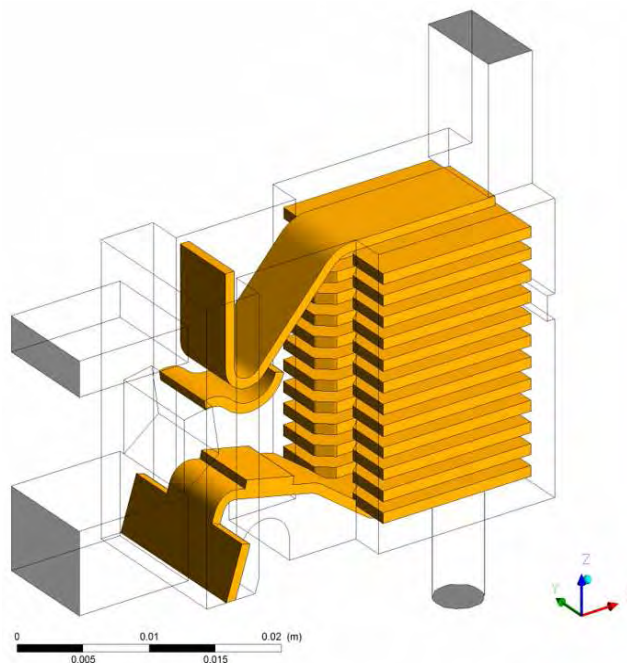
Dimensions de la géométrie industrielle C1.
